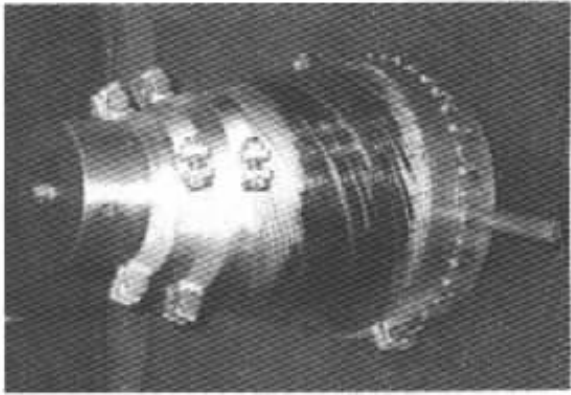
焊后的复杂曲面不锈钢薄壁工件
